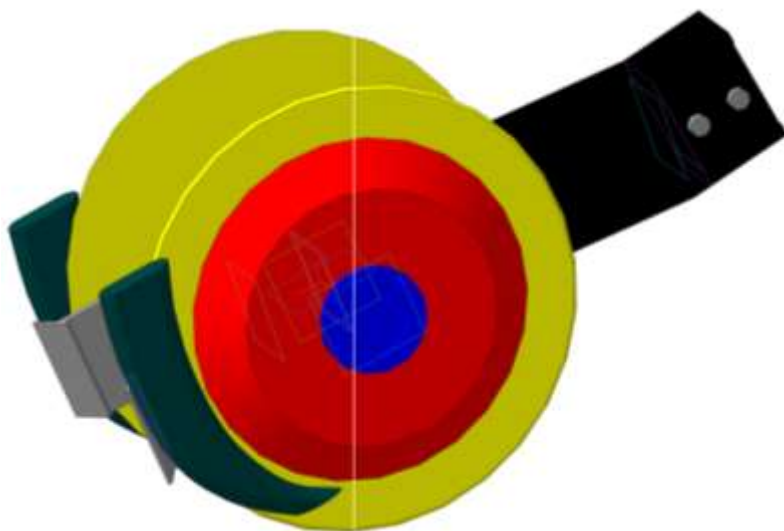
Трехмерная модель двухдискового сошника с усеченными коническими ребрами-бороздкообразователями
